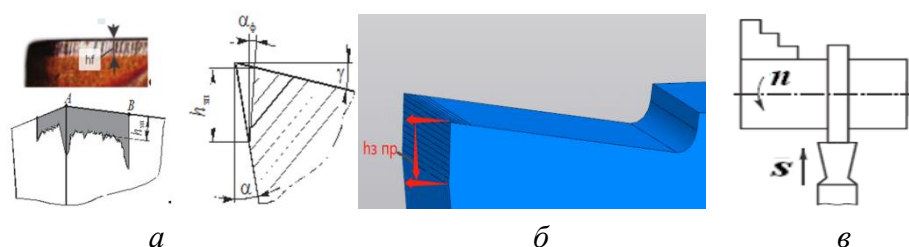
Режущая пластина с износом по задней поверхности (*а*), 3Д модель режущего клина с искусственной фаской по задней поверхности (*б*) и схема прямоугольного свободного резания на примере обработки диска с радиальной подачей резца (*в*)
